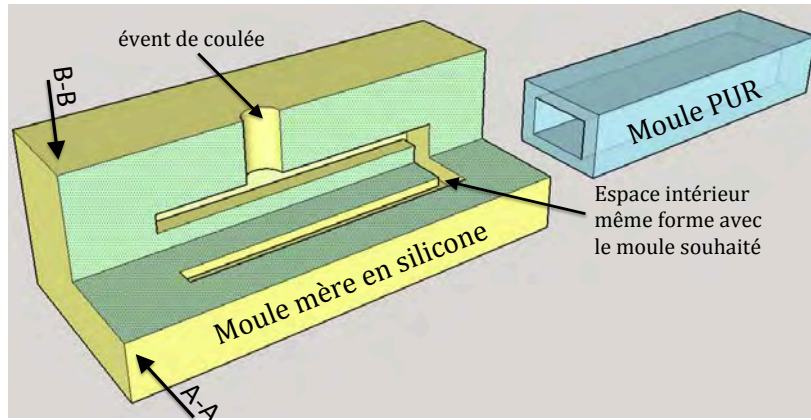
Moule-mère de silicone qui nous permet de réaliser le moule par un coulage
